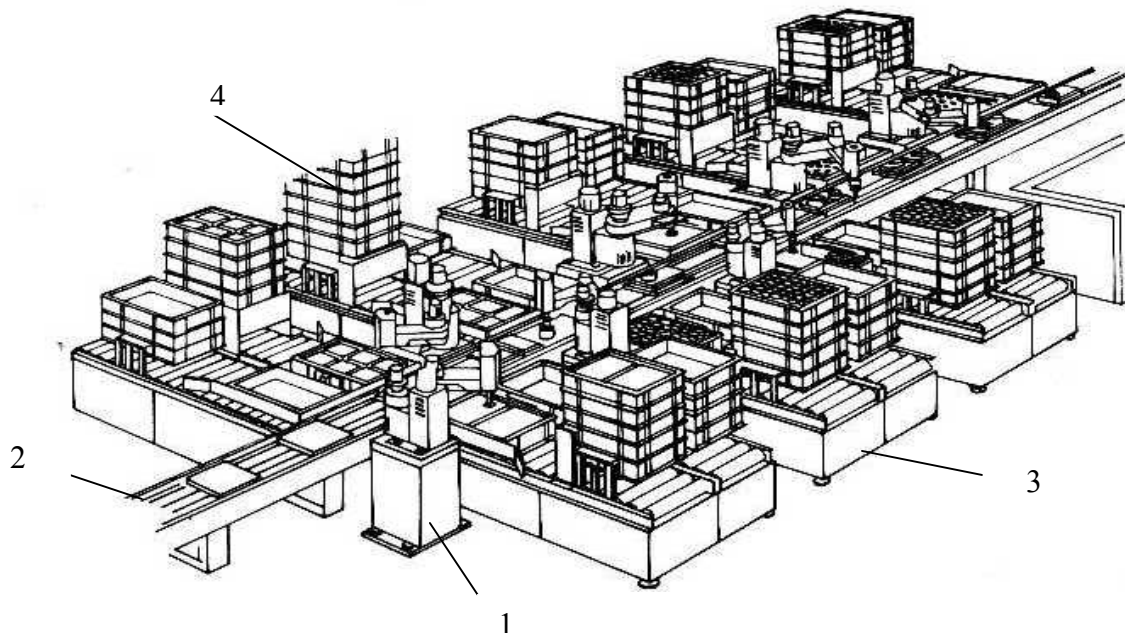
Robotizovaný montážny systém pre montáž dverí automobilu
